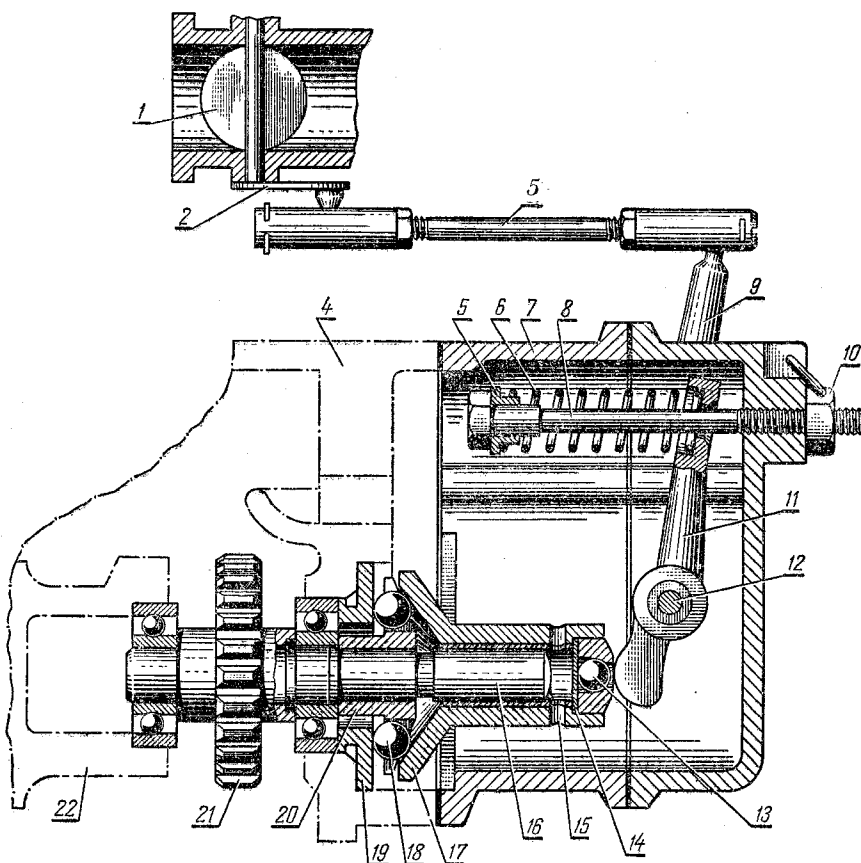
Однорежимный шариковый центробежный регулятор пускового двигателя ПД-10У:
